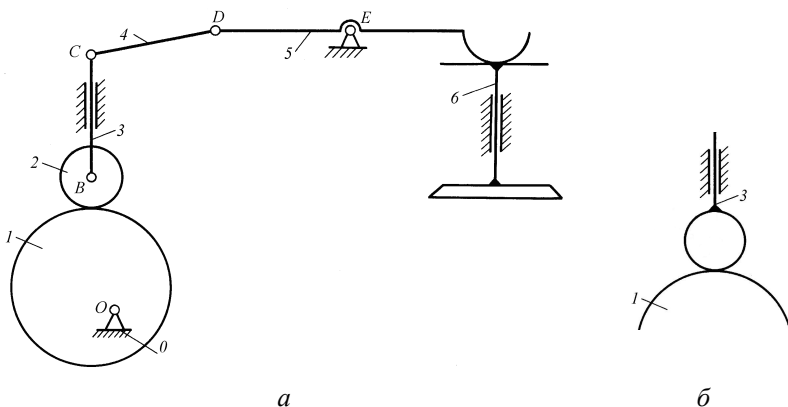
Газораспределительный механизм двигателя вертолётa
